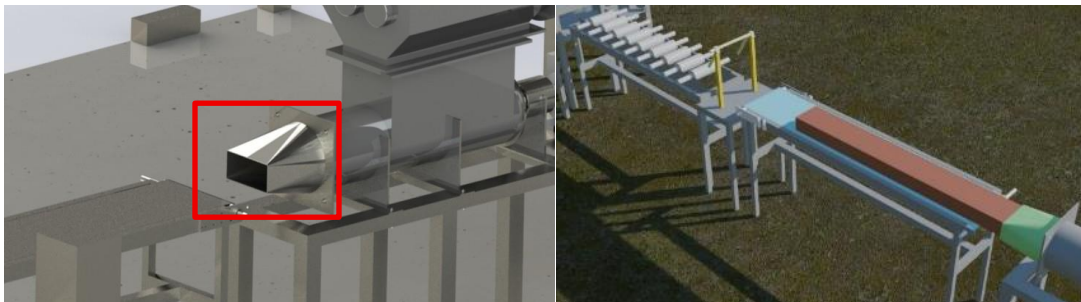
y 4. Conjunto extrusor moldeador de arcilla
